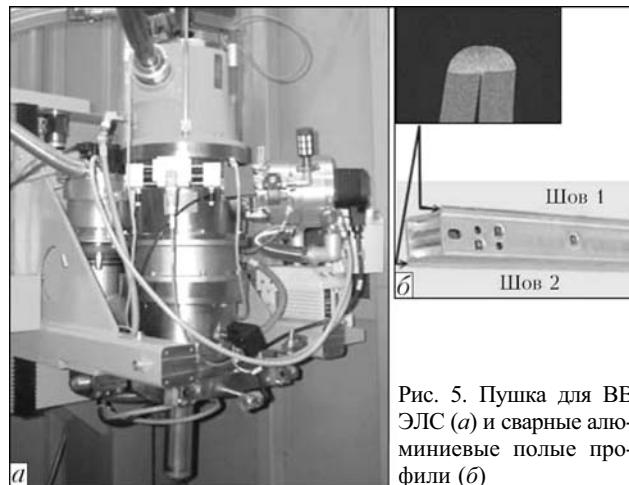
Пушка для ВВ ЭЛС (а) и сварные алюминиевые полые профили (б)
